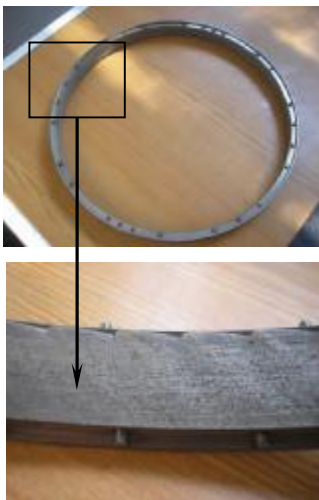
Кольцо рабочего колеса компрессора ГТД после эксплуатации (видны сколы и пористость поверхности)
